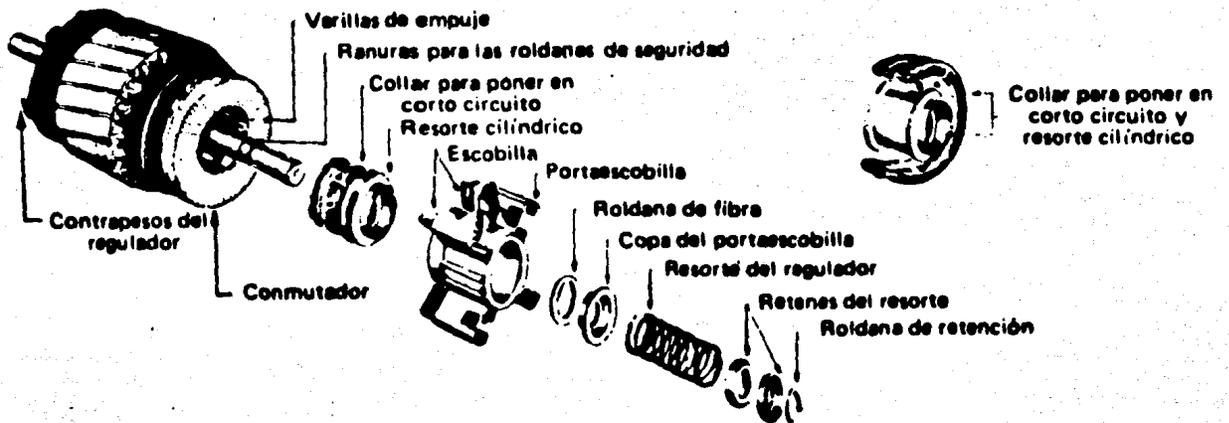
Conmutador radial y dispositivo centrífugo levantador de escobillas.
